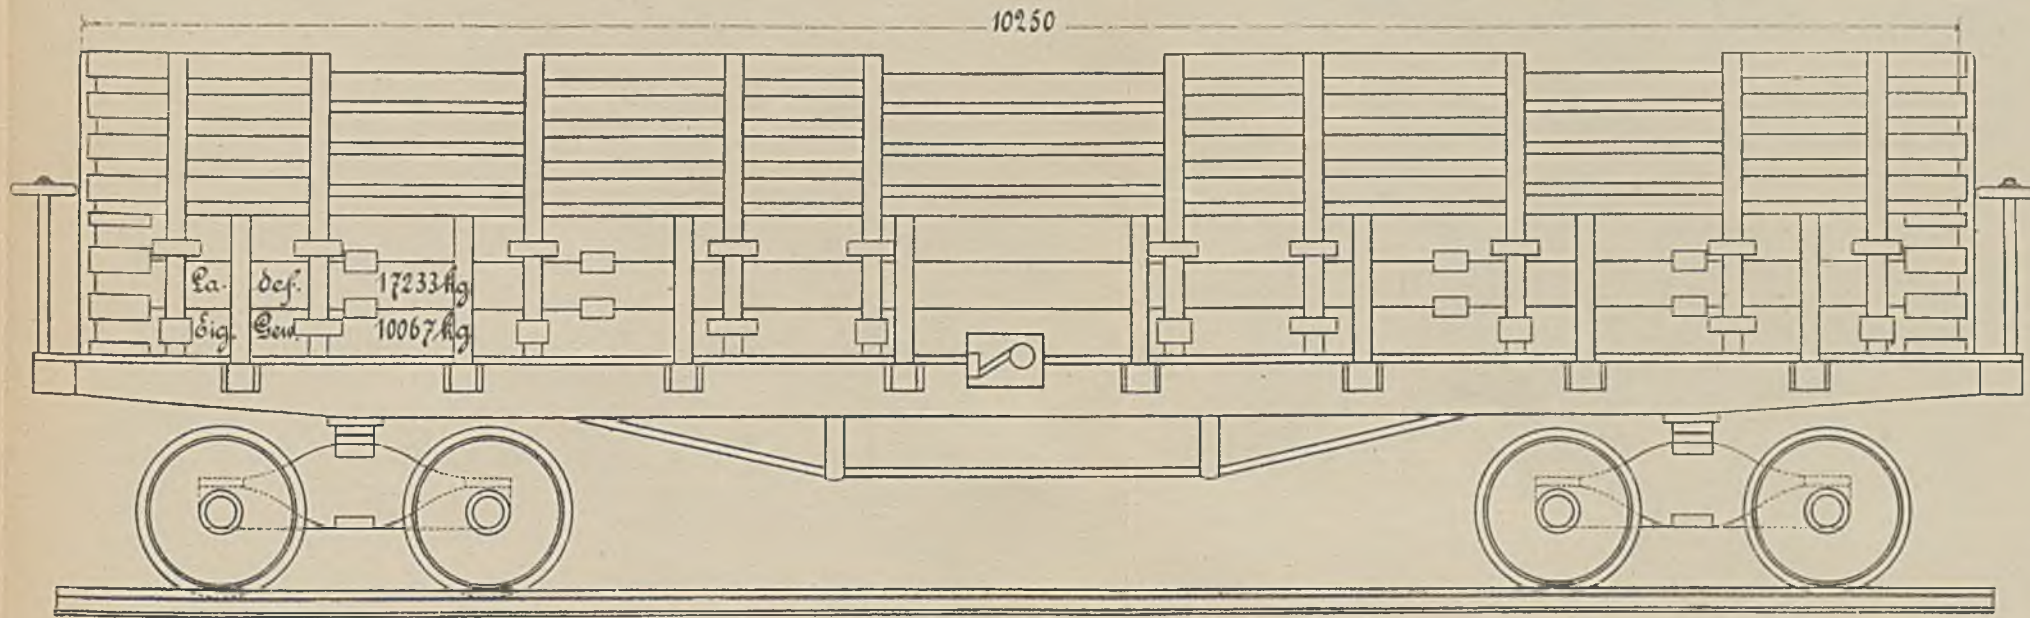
und 9. Erzwagen mit beweglichen Bodenklappen.
